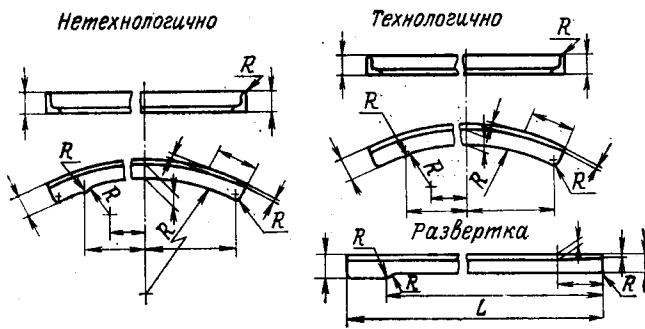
Простановка размеров на длинномерные детали.
